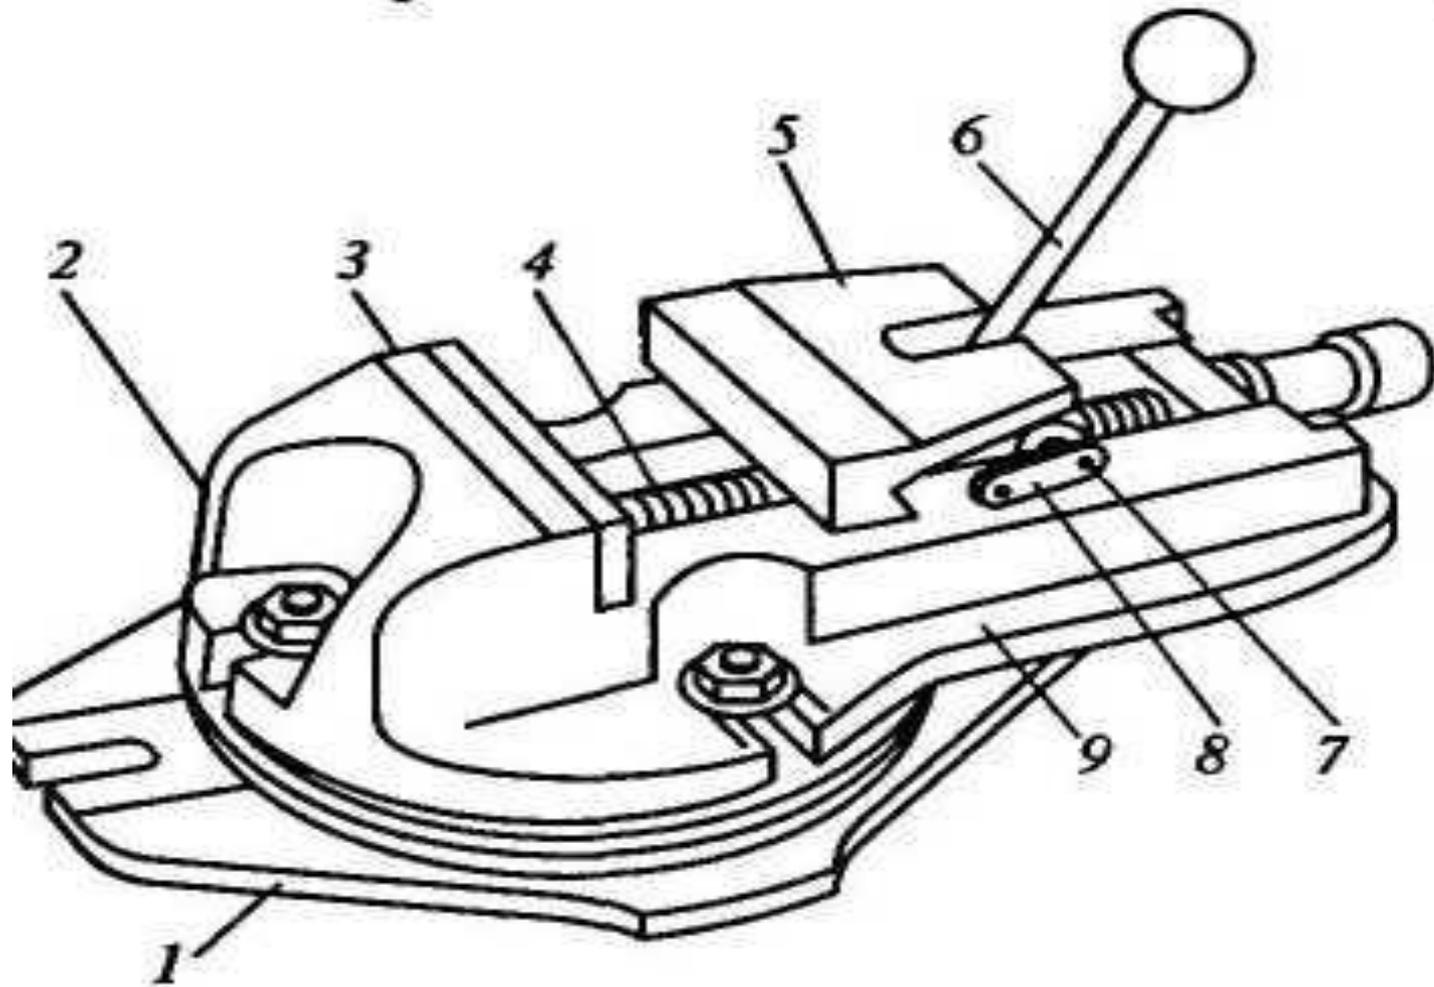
Быстродействующие машинные тиски: 1 - корпус; 2 - поворотная часть; 3 - неподвижная губка; 4 — установочный винт; 5 - подвижная губка; 6 - рукоятка; 7 - эксцентриковый вал; 8 - двойной кулачок; 9 - основание
